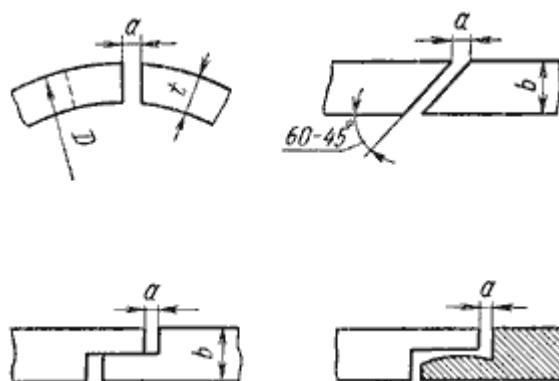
Типы стыковых замков металлических колец: а - прямой; б - косой; в, г - ступенчатый
